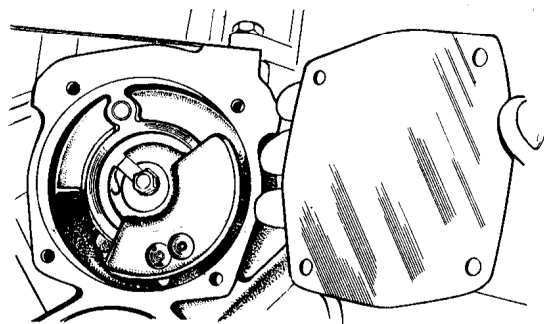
Вид на балансирующий механизм со стороны маховика при снятой крышке балансирующего вала
